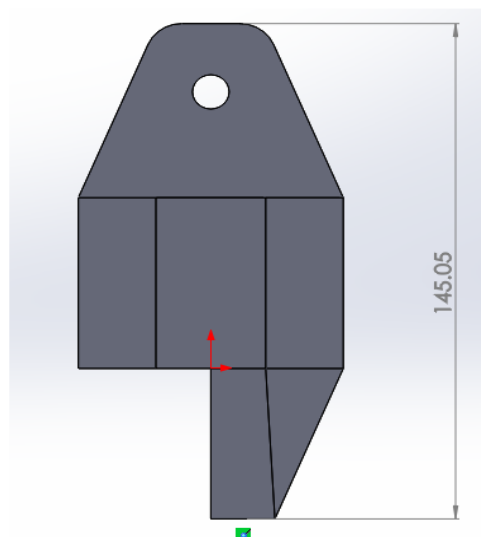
Vista Frontal módulo com dimensão de comprimento em milímetros (0.145 metros)
